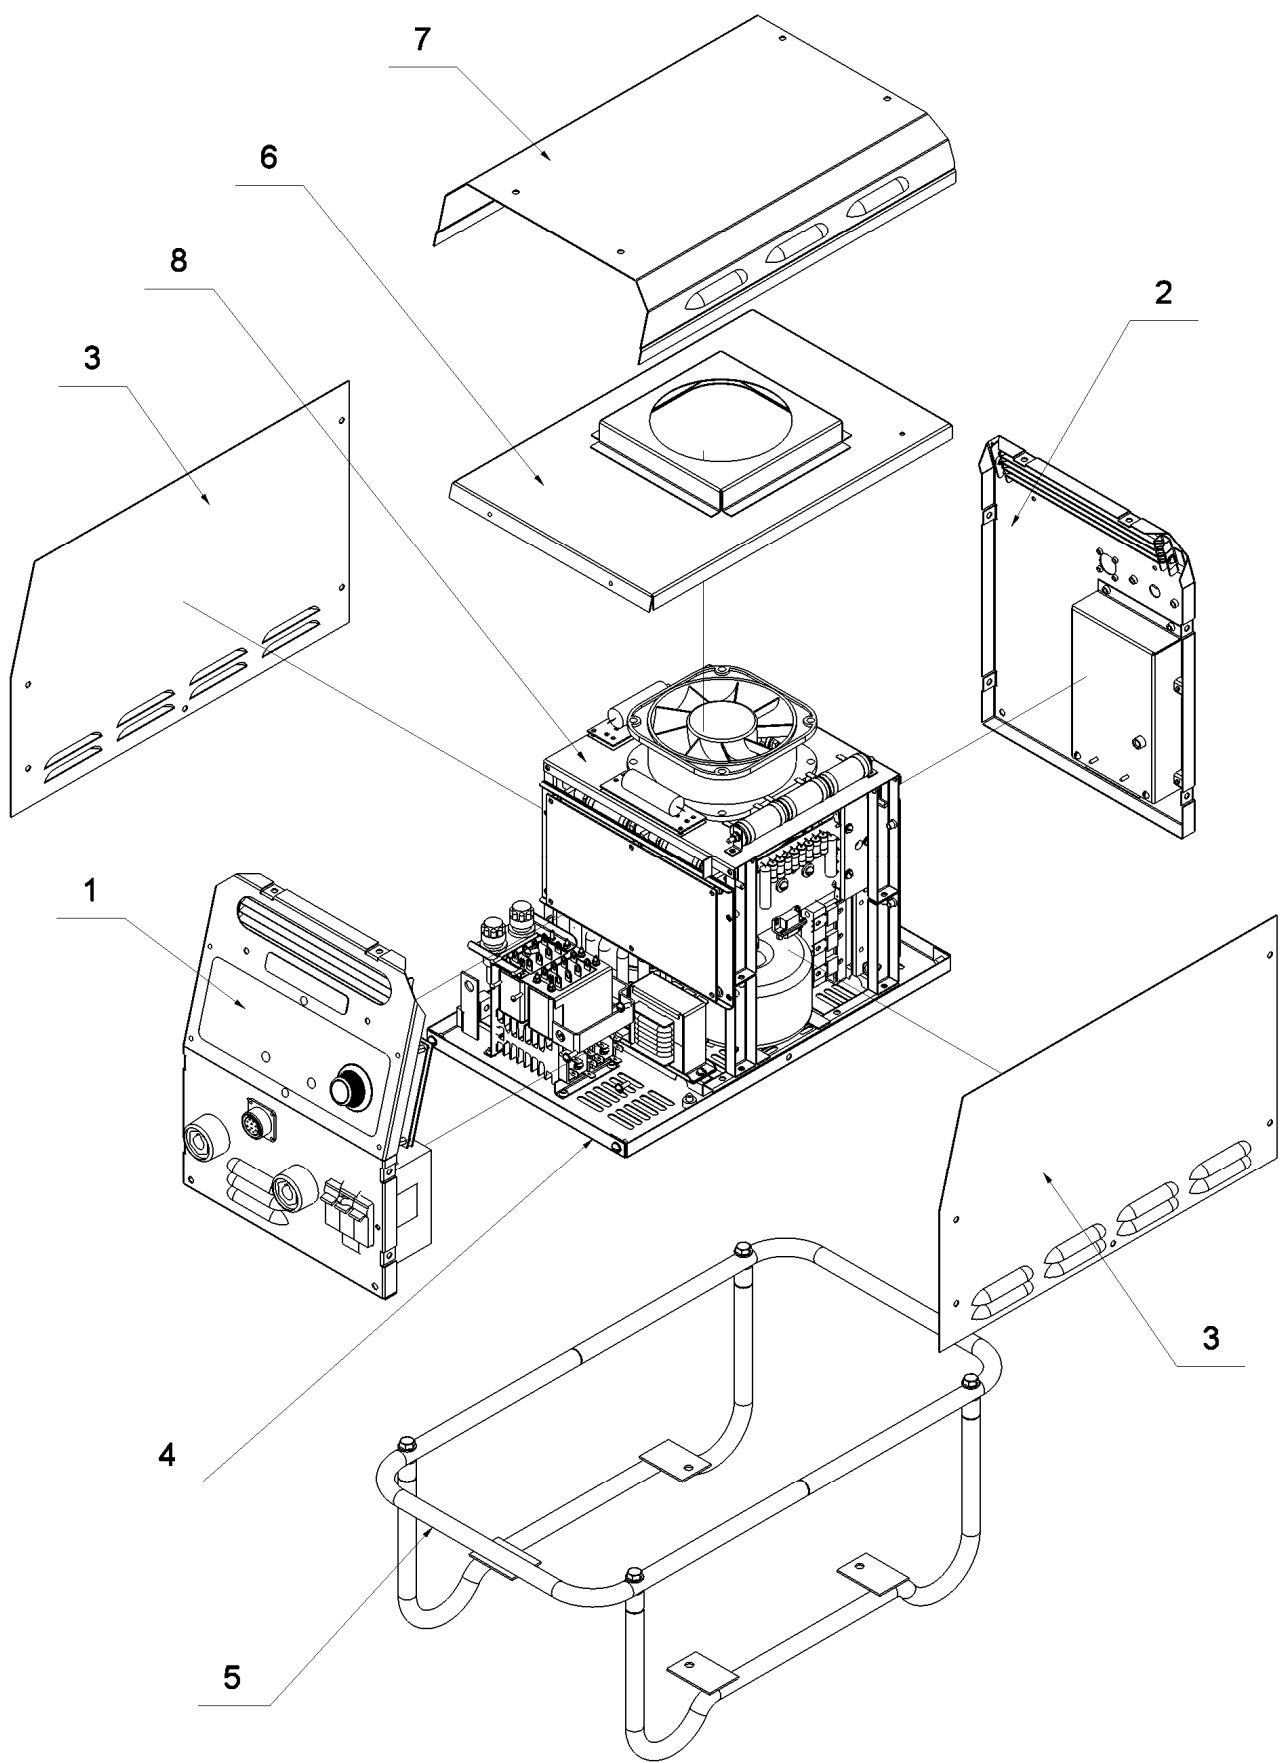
Конструкция корпуса сварочного источника.
